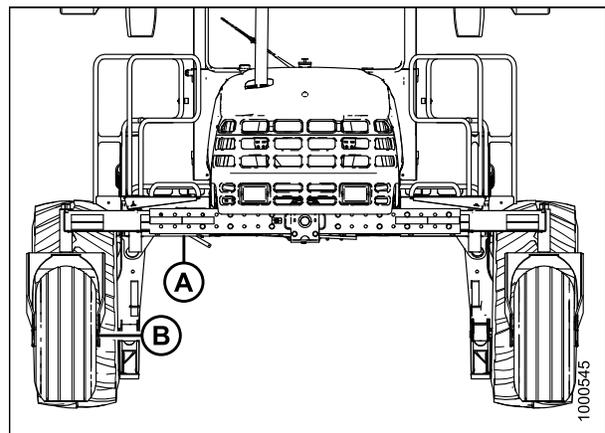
Самоустанавливающиеся колеса и балансир (вид в положении двигателем вперед)
